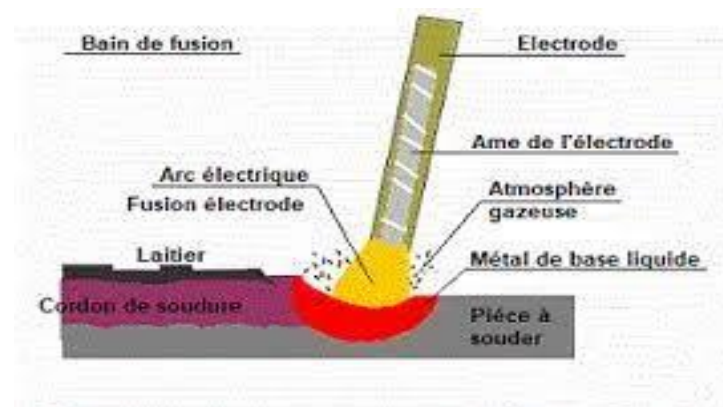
Soudage à l'arc avec électrode enrobée. [32]
